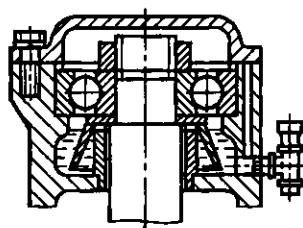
Фитильная смазка подшипников вертикального вала при верхнем расположении резервуара (1 – фитиль)
